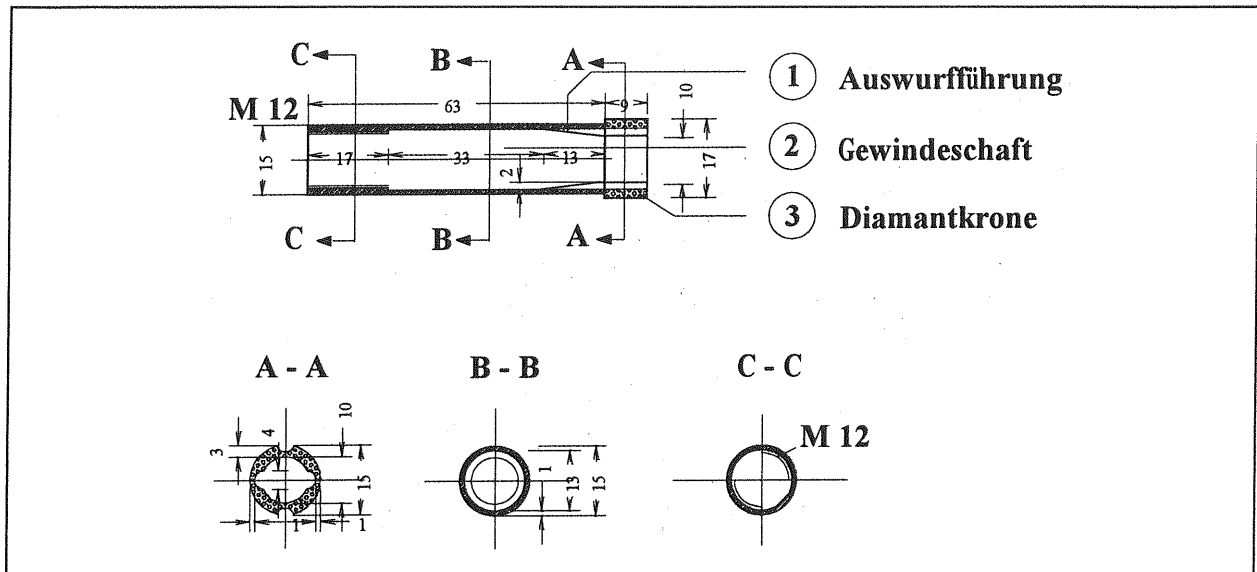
Diamantbohrkrone mit Gewindeschaftansatz
